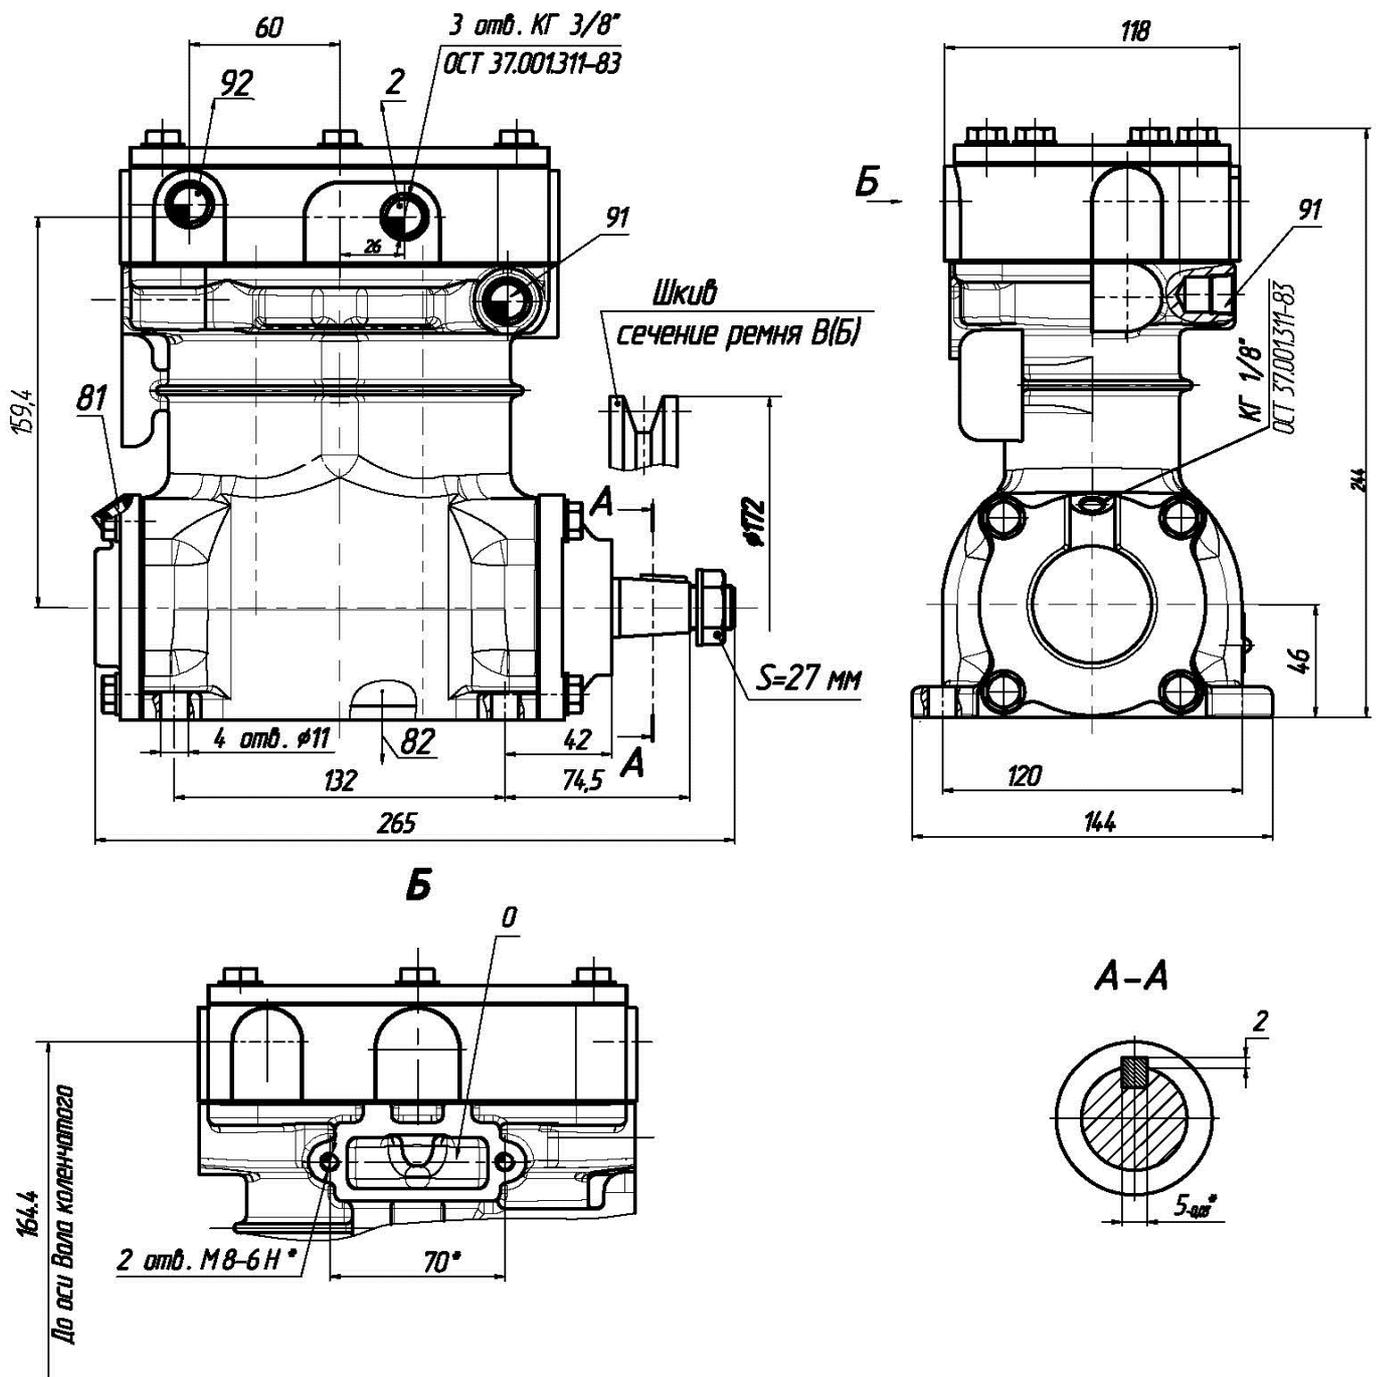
Присоединительные и установочные размеры компрессора AM.3509012-161. Маркировка отверстий: 0 — всасывание; 2 — нагнетание; 81 — подвод масла; 82 — слив масла; 91 — подвод охлаждающей жидкости; 92 — отвод охлаждающей жидкости.
